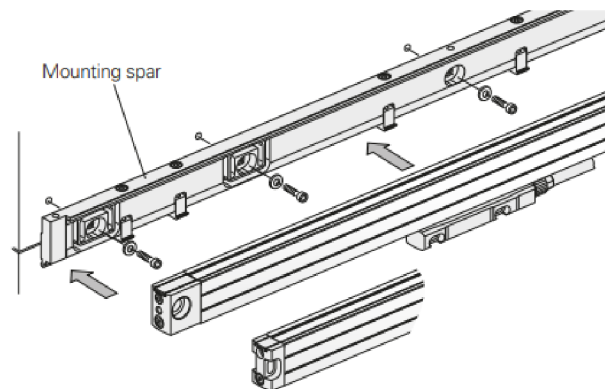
Upnutie a geometrická tolerancia [3]
